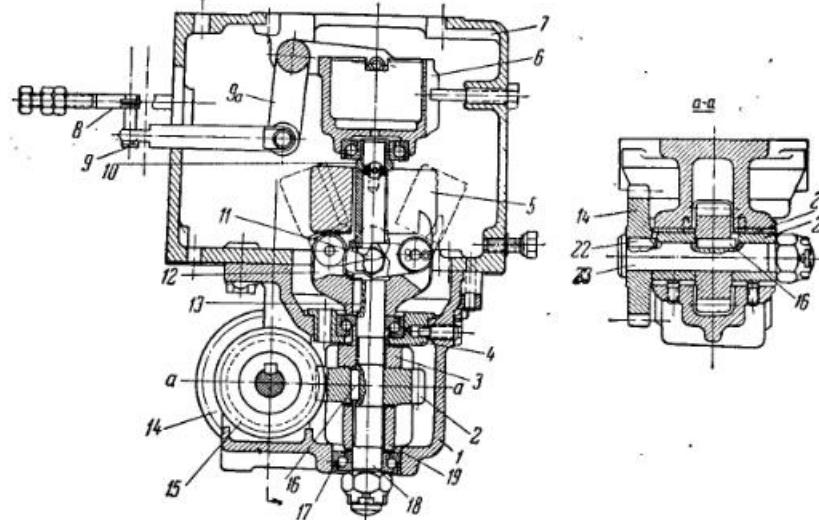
Регулятор числа оборотов двигателей типа NVD-24:
